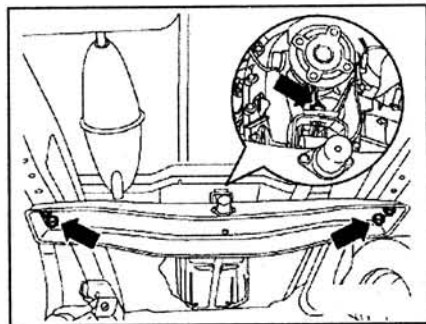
Открутите болты крепления (стрелки) поперечной балки двигателя/коробки передач и снимите ее.
